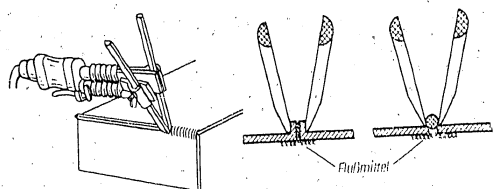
Weibel- (Fesa-) Schweißverfahren
